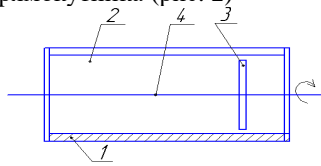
Розгорнутий вид шнекового пресу прямокутної форми; 1 – зеєрна планка; 2 – канал пресу; 3 – поршень; 4 - вал
